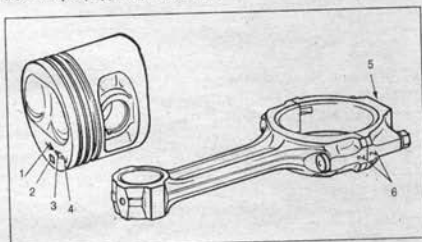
Маркировка поршня и шатуна: 1 – стрелка для ориентирования поршня в цилиндре; 2 – ремонтный размер; 3 – класс поршня; 4 – класс отверстия для поршневого пальца; 5 – классы шатуна по массе и по отверстию в верхней головке; 6 – номер цилиндра
